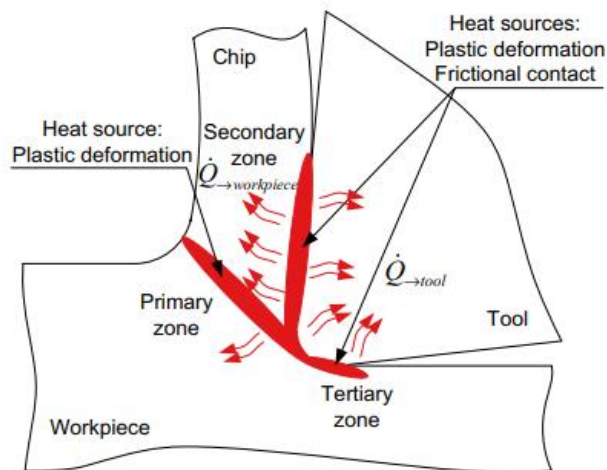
Зони генерування тепла під час формування стружки при механічному обробленні [14].
